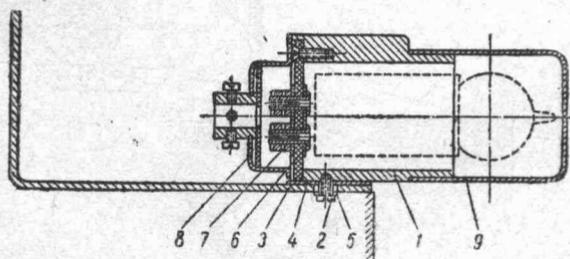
Фотоячейка: 1 — корпус; 2 — винты; 3 — угольник; 4 — прокладка; 5 — втулка; 6 — панель; 7 — гнездо; 8 — экранирующий колпачок; 9 — колпачок
